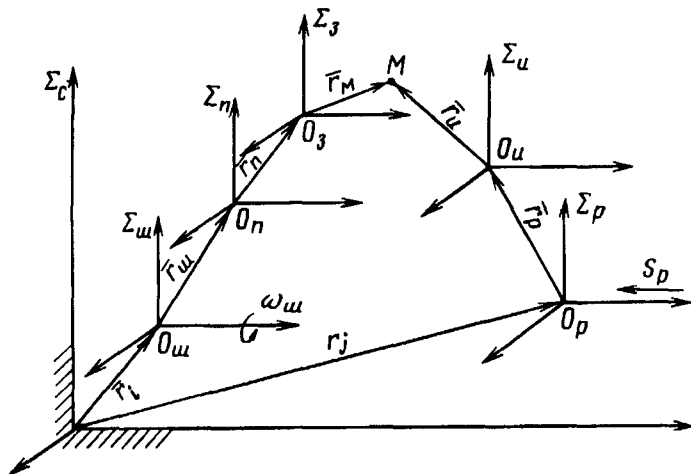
Эквивалентная схема динамической настройки токарного станка
